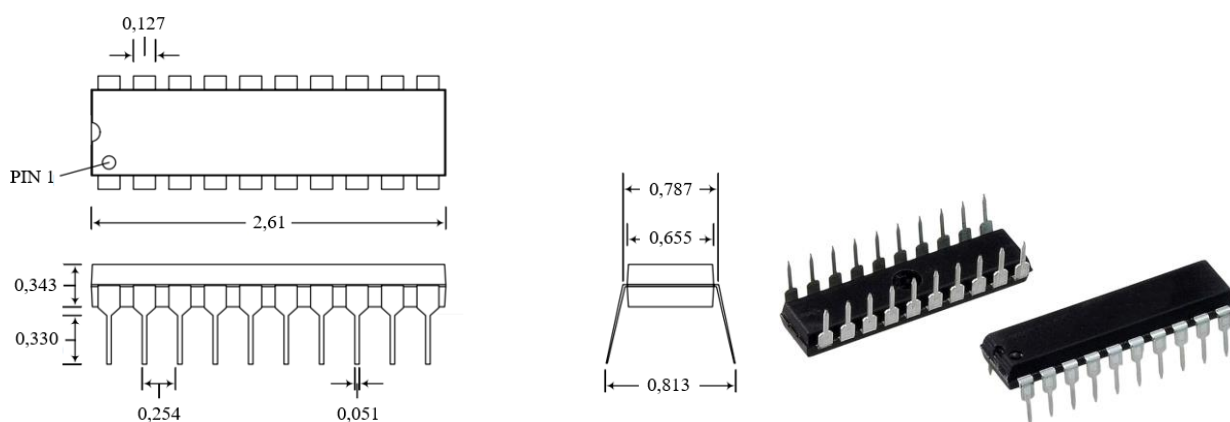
Пластиковый двухрядный корпус (PDIP) с 20 контактами (размеры указаны в см)
